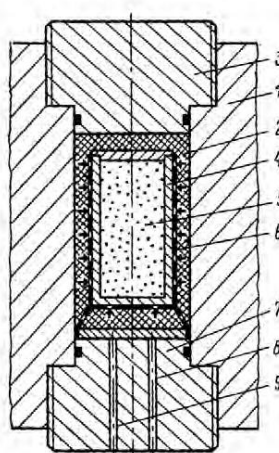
Основная схема изостатического прессования: 01 - сосуд высокого давления; 2 - жидкость под высоким давлением; 3-верхний затвор; 4 - эластичная форма; 5-прессовый порошок; 6 - перфорированная корзина; 7- нижние ворота; 8 - высокое давление; 9 - сточные воды
